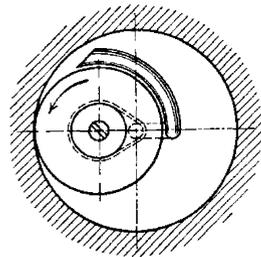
Wasserzuführungsrohr beim Innenschleifen.
